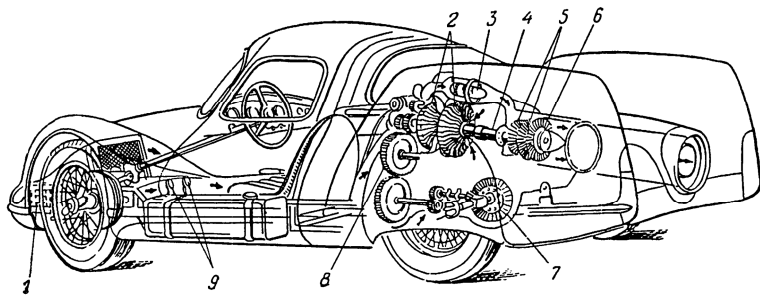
Схема газотурбінного автомобіля «Фіат»: 1 – впуск повітря; 2 – компресор; 3 – камера згоряння; 4 – вал; 5 – компресорна турбіна; 6 – тягова турбіна; 7 – диференціал; 8 – редуктор; 9 – педалі газу і гальма
